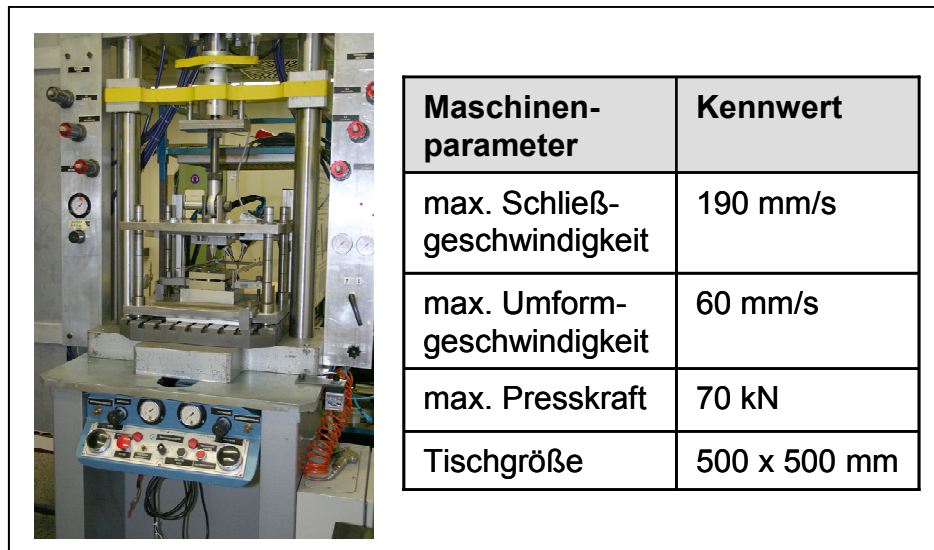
Zum Thermoformen verwendete hydraulische Umformpresse
